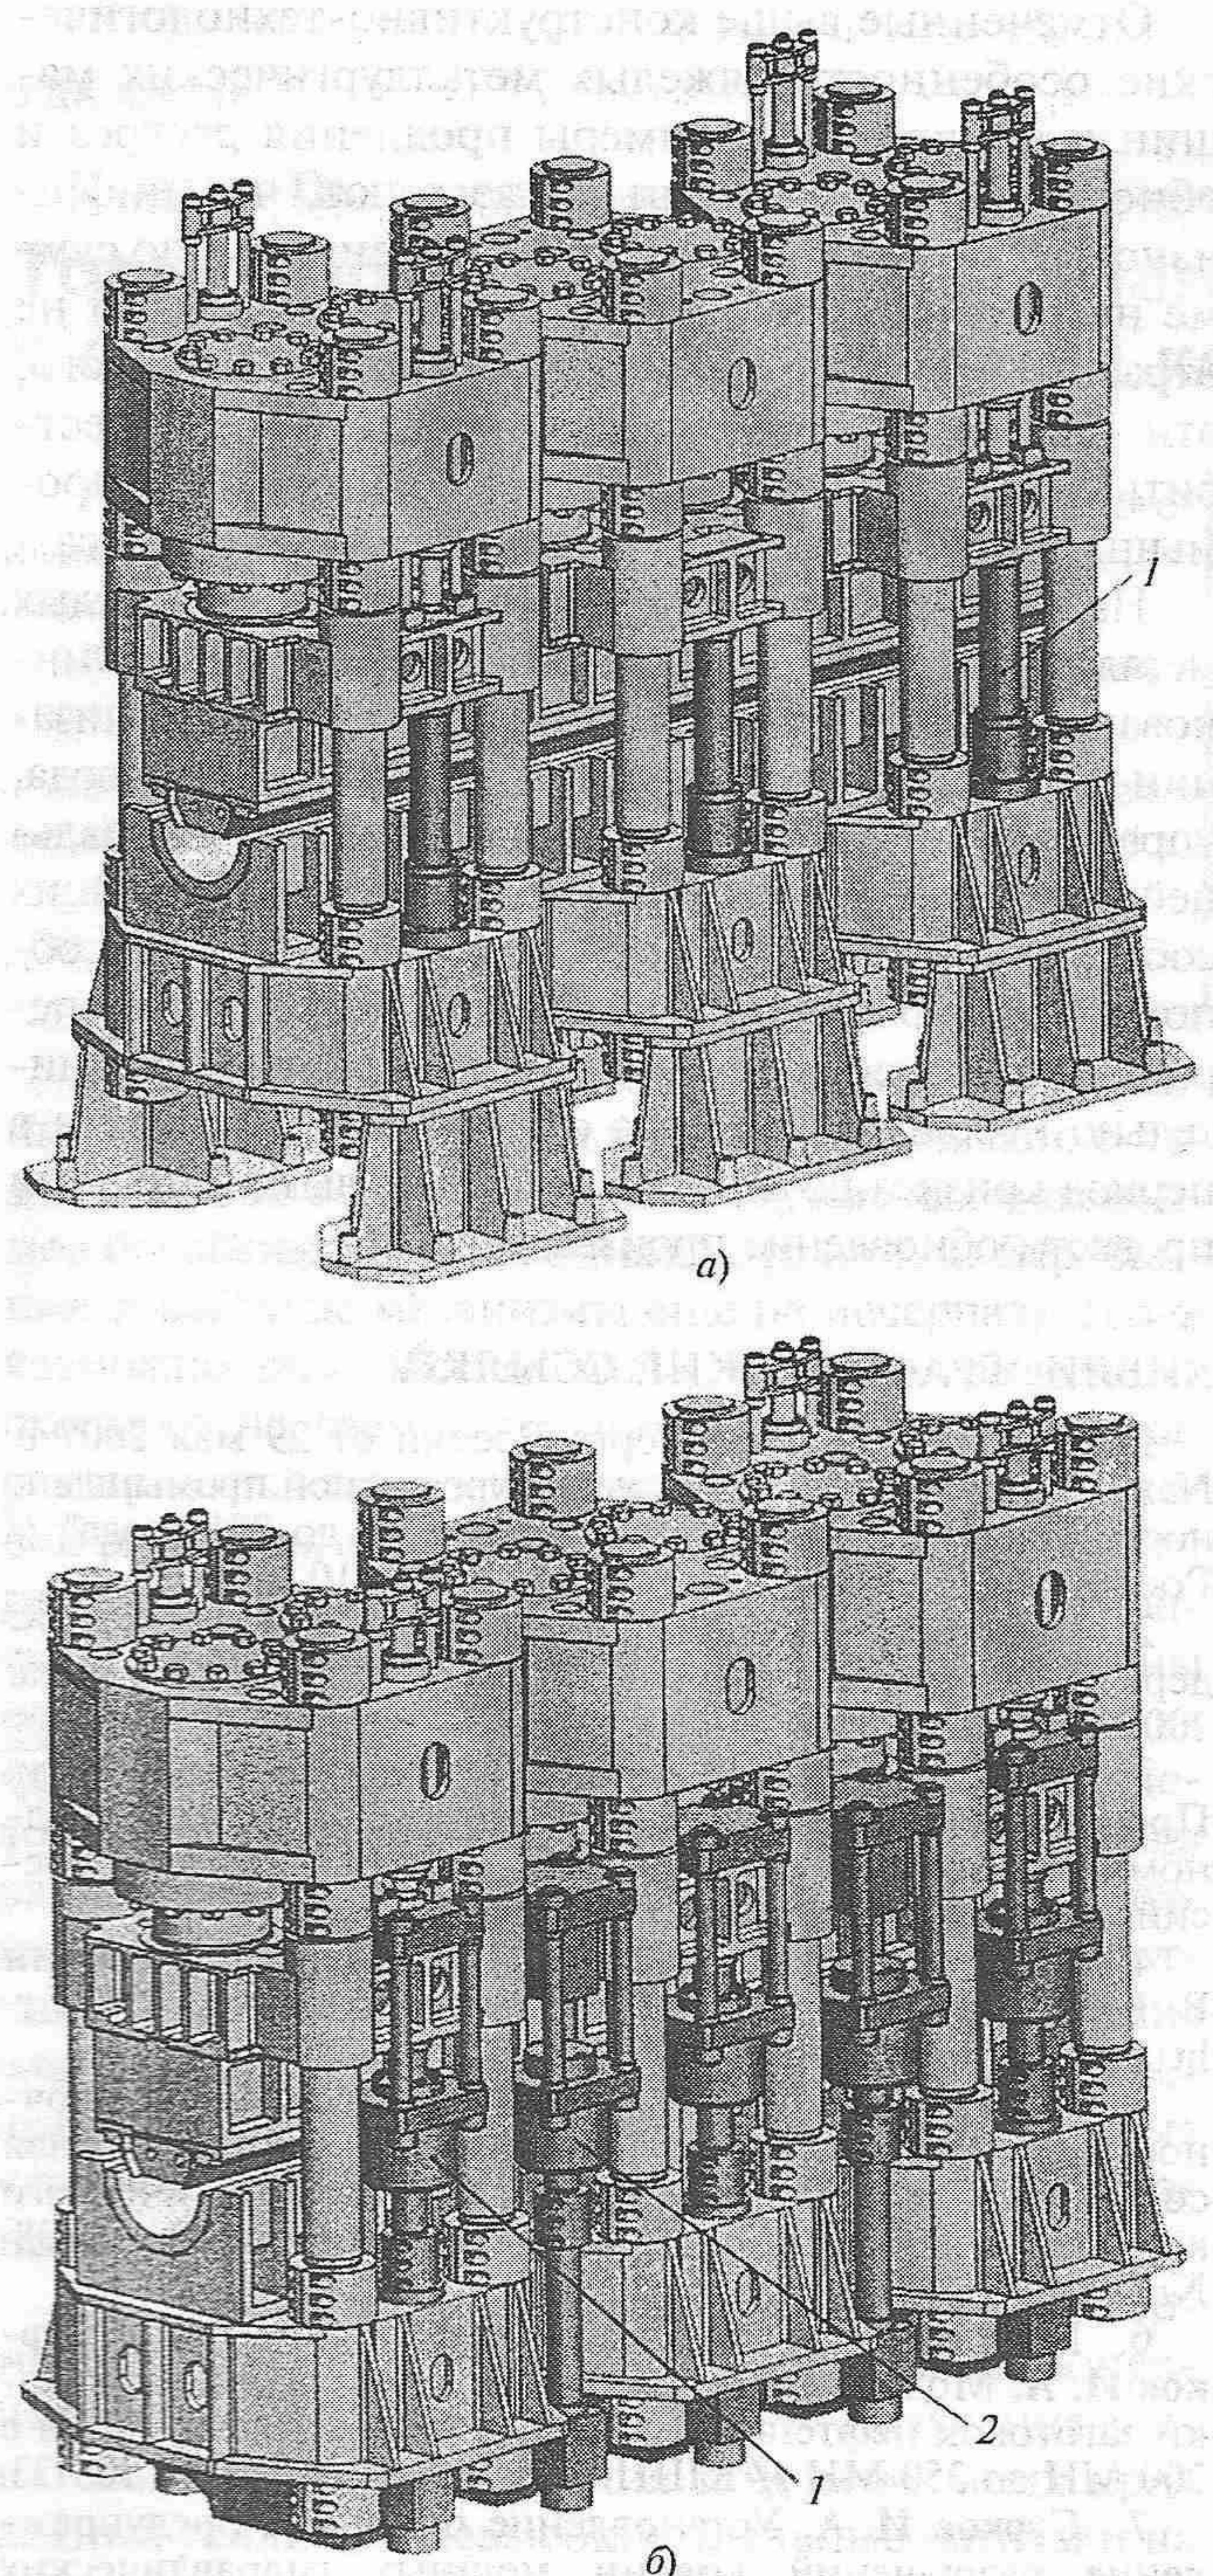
Прессы окончательной формовки заготовок нефтегазовых труб диаметром 1020–1120 м:
